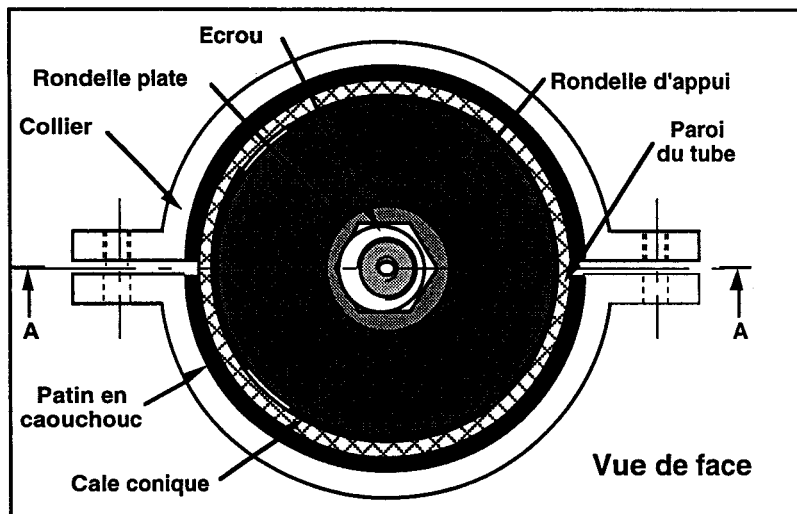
Systèmes d'étanchéité (bouchon) et de fixation des structures tube - Vue de face
